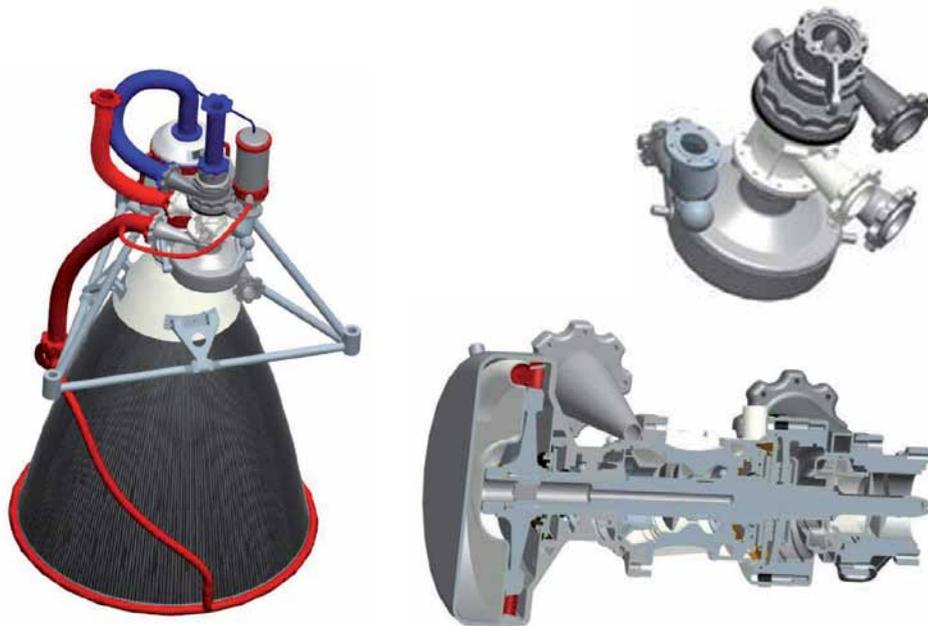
Motor L75, com vista ampliada e em corte da turbobomba
